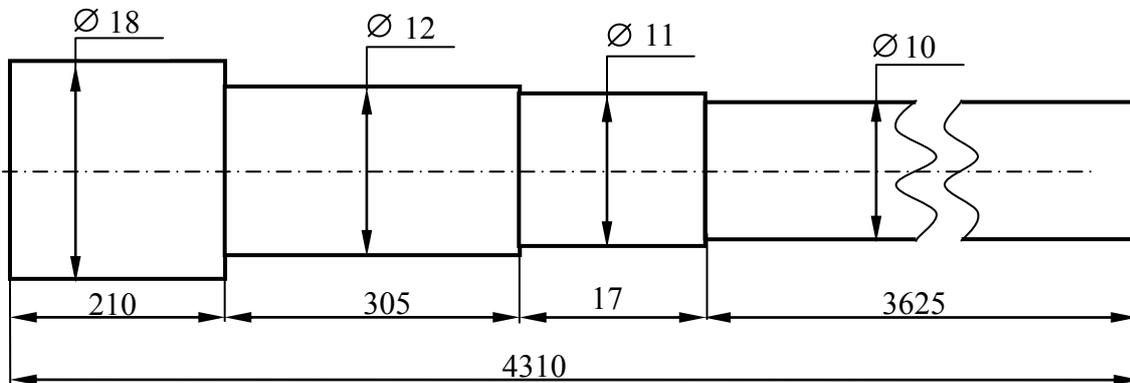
Эскиз ведущего вала привода механизма передвижения рельсовой грузоподъемной машины
